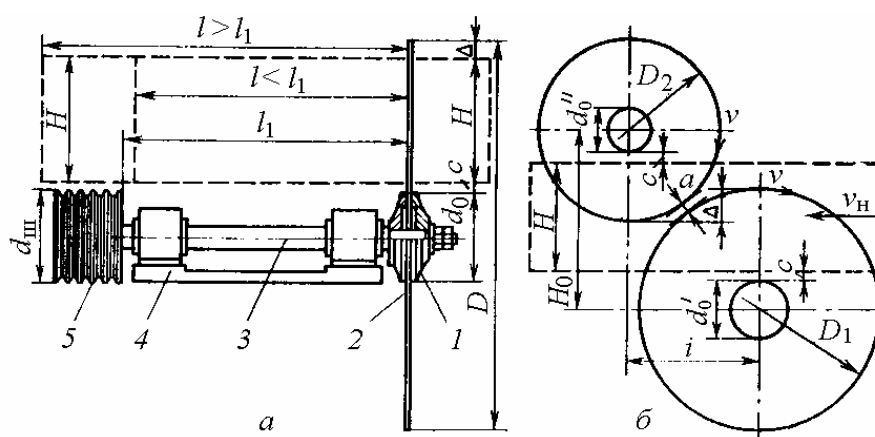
Пильный механизм: *а* – устройство пильного механизма; *б* – схема расположения пил в одном пропиле; 1 – фланцы; 2 – круглая пила; 3 – пильный вал; 4 – опоры; 5 – приводной шкив
